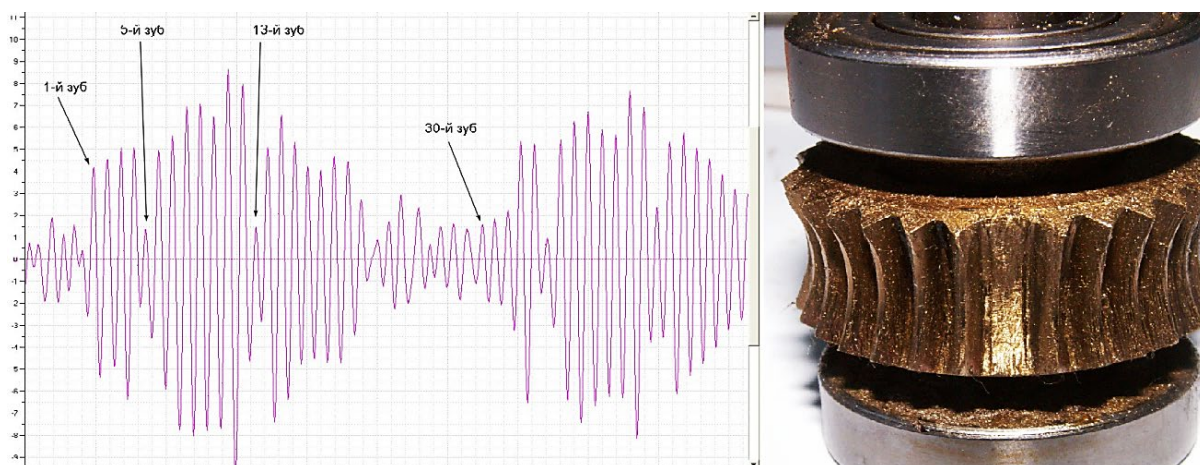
Сигнал дефектного привода (отсутствие зубьев шестерни) [Defective drive signal (missing gear teeth)]
